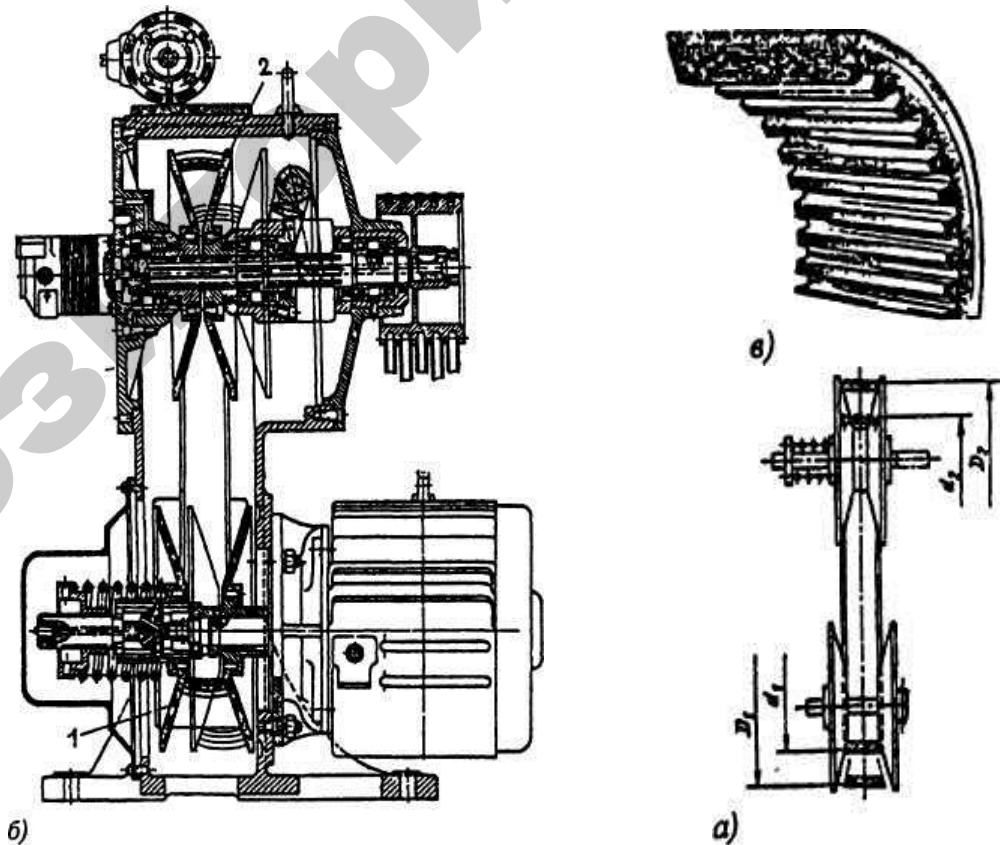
Клиноременный вариатор: а — принципиальная схема; б — конструкция ремня вариатора; в — конструкция вариатора с одним широким ремнем; 1 — ведущий прижимной шкив; 2 — автоматически регулируемый шкив
